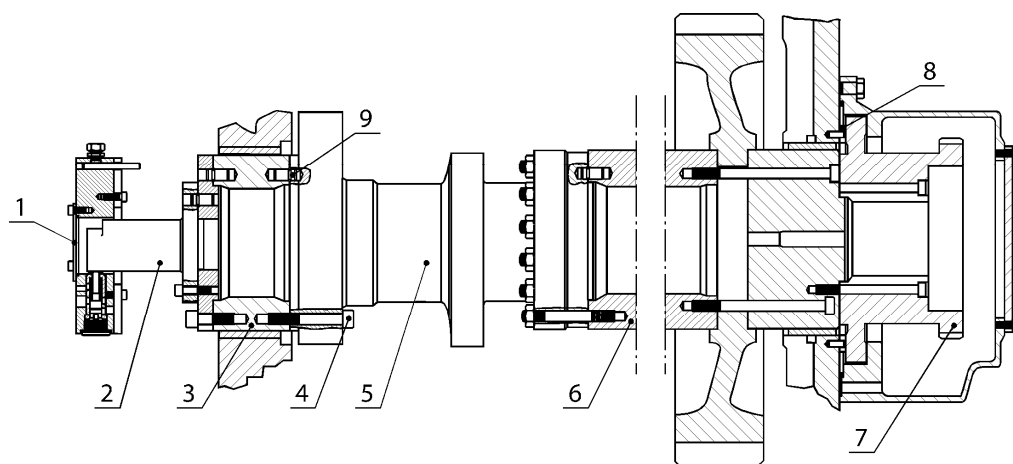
Розподільний вал двигуна. 1 – кришка; 2 – подовжувальна секція для розподільника пускового повітря; 3 – підшипникова цапфа; 4 – гвинт; 5 – секція распределу; 6 – подовжувач; 7 – шестерня для приводу регулятора; 8 – упорний підшипник 9 – направляючий штифт
